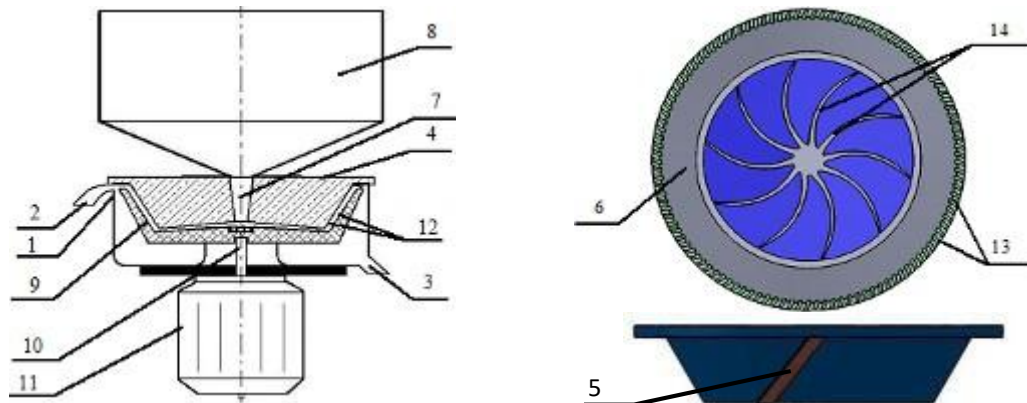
Конструктивно-технологічна схема подрібнювача замоченого зерна сої включає рухомий абразивний диск (вигляд зверху) та нерухомий абразивний диск (вигляд збоку) і складається з таких елементів: 1 – корпус; 2 – патрубок для виведення окари; 3 – патрубок для відведення суспензії; 4 – нерухомий абразивний диск; 5 – скребок; 6 – сито; 7 – подаючий патрубок; 8 – завантажувальна ємність; 9 – рухомий абразивний диск; 10 – вал; 11 – привід; 12 – наскрізні канали для відведення рідкої фракції; 13 – криволінійні борозенки; 14 – криволінійні радіальні канали.
